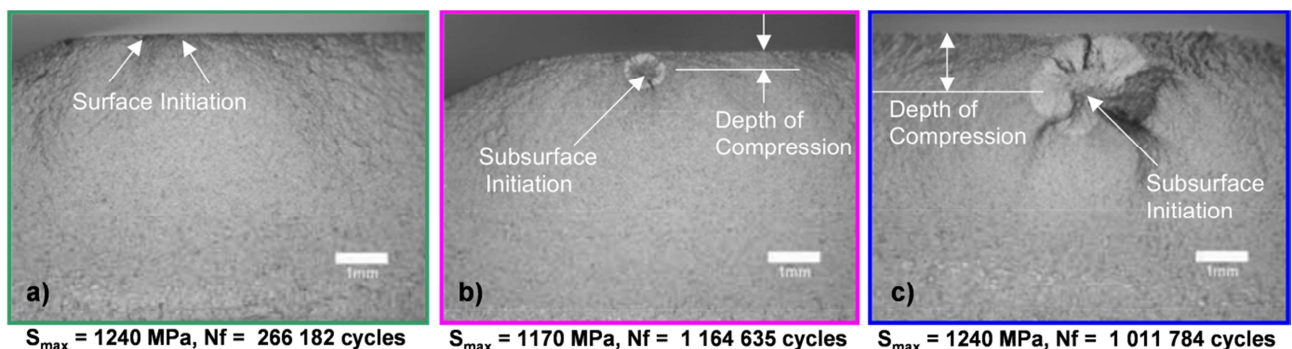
Fractographies des initiations à la fissure pour des éprouvettes : a) électropolie, b) grenailée par air comprimé et c) traitée par LPB [Cammett et al., 2005].
